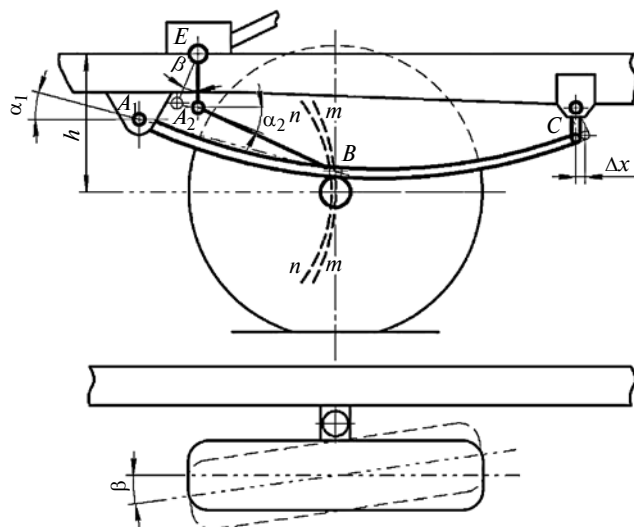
Схема передней рессорной подвески и привода управляемого колеса:
